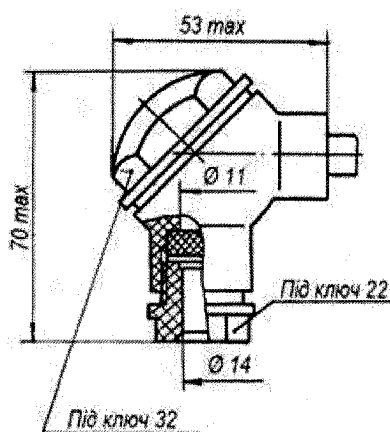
Кресленик зовнішньої частини ТХА-1090, ТХК-1090 з головкою ПБВИ.408724.001-01 СБ
